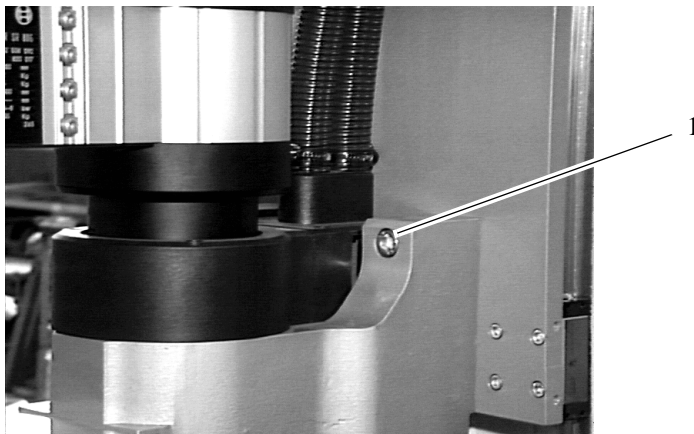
Befestigungsschrauben Roboterkonsole
